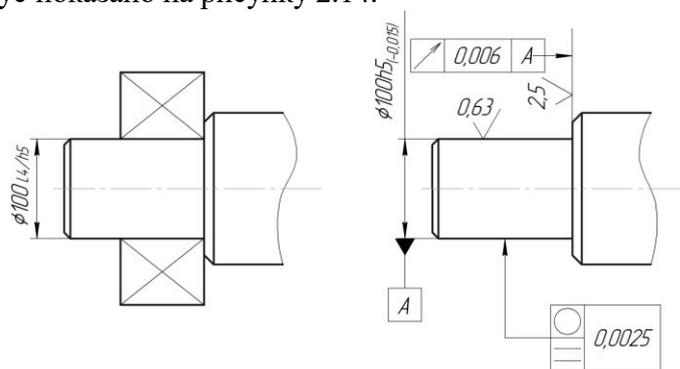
Ескіз посадки внутрішнього кільця підшипника на вал.
